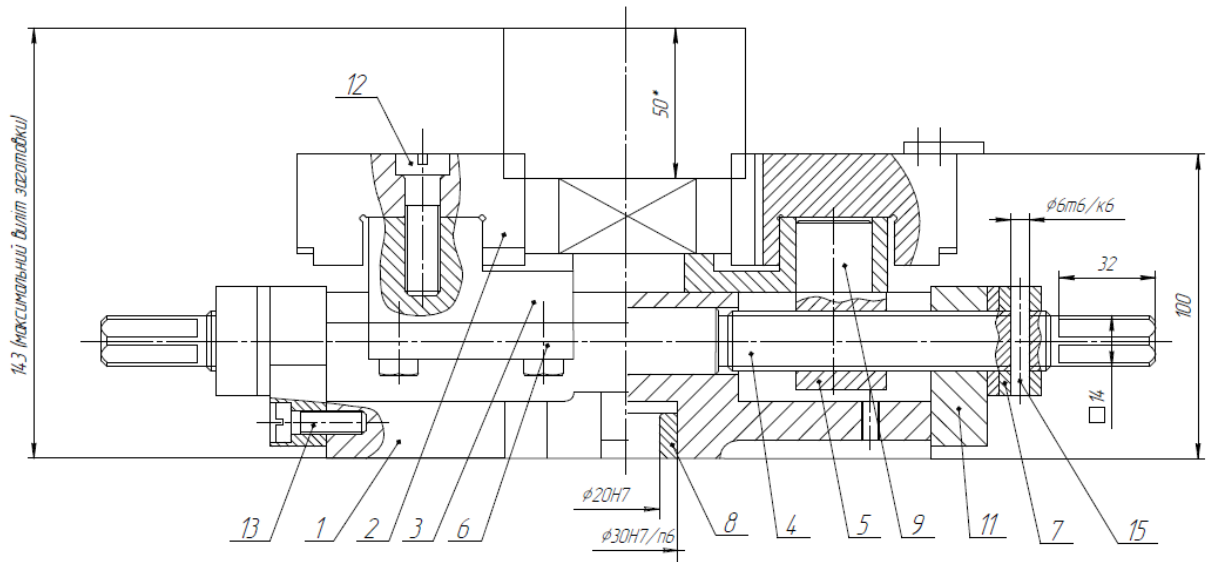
Загальний вигляд переналагоджуваних лещата
